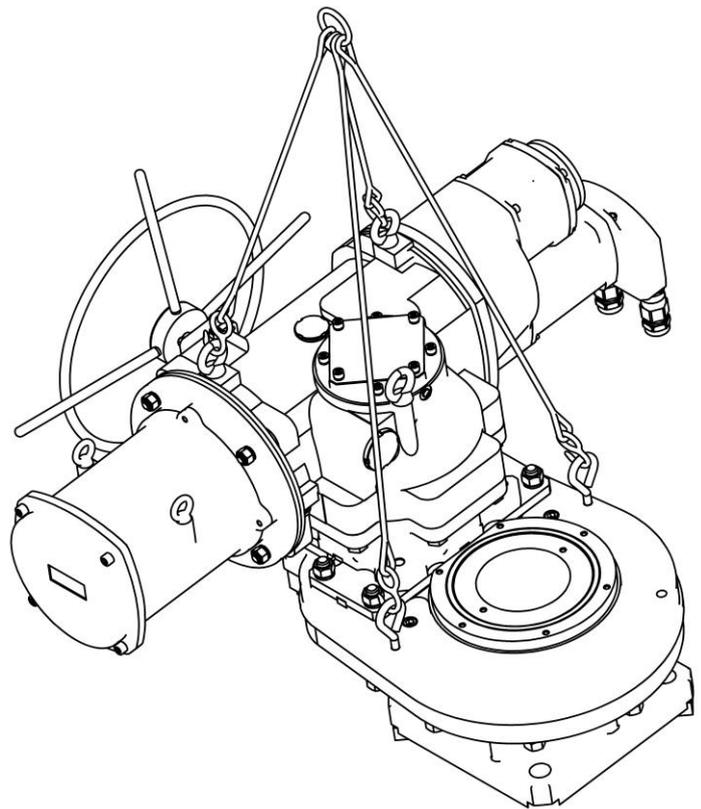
д – Схема строповки привода конструктивной схемы 430
